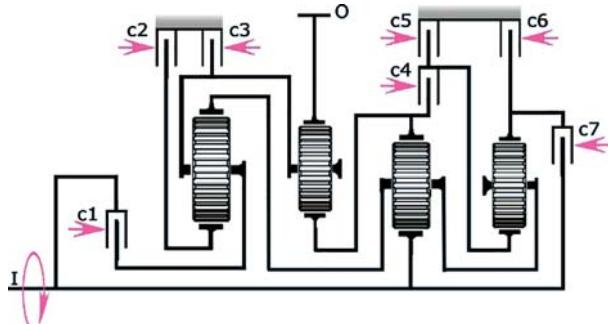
Кинематическая схема 10-ти ступенчатой планетарной коробки передач фирмы Honda Motor:
